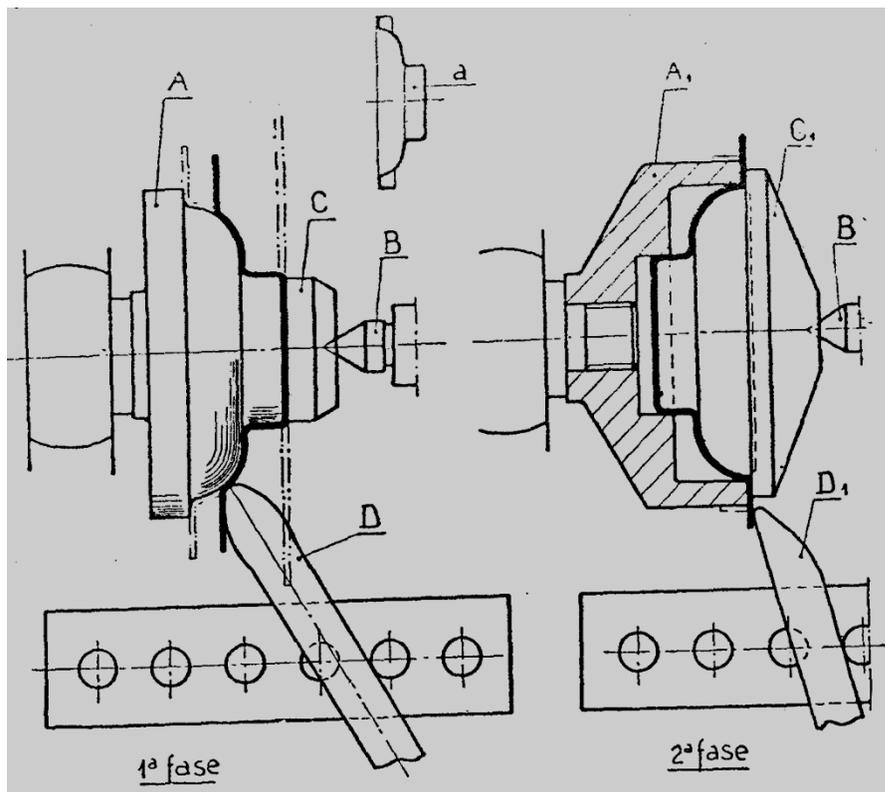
Embutido realizado en el torno, de una chapa, [3].
